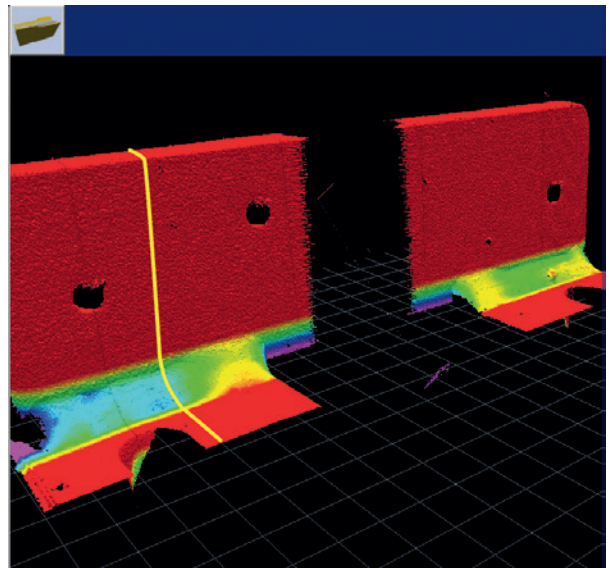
Schweißnahtkontrolle mit dem M2-iLAN-Laserscanner der MEL (mit freundlicher Genehmigung der MEL GmbH)
